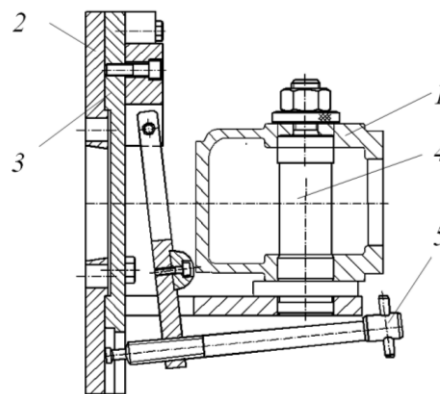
Схема спеціального верстатного пристрою для підрізання торця та розточування отвору у корпусній заготовці з базуванням по торцю та основному отвору заготовки: 1 – заготовка; 2 – планшайба; 3 – диск; 4 – циліндричний палець; 5 – притискний елемент для вибору зазору по отвору заготовки
